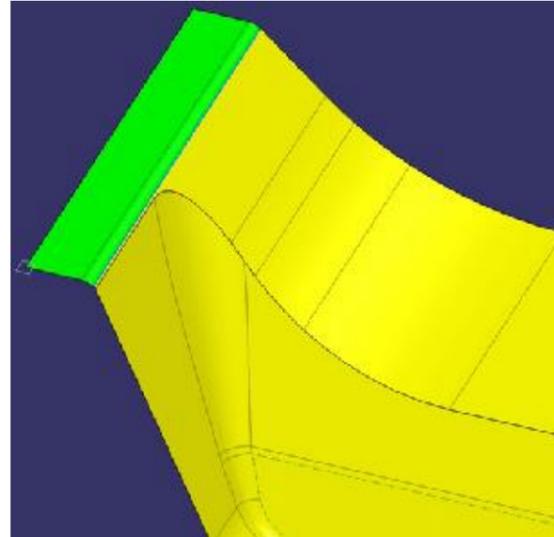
Vordere Flanschfläche mit Abrundungsradius R5, danach nur hinteren (oder beide) Flächenverbund(e) zweckmäßig beschneiden
